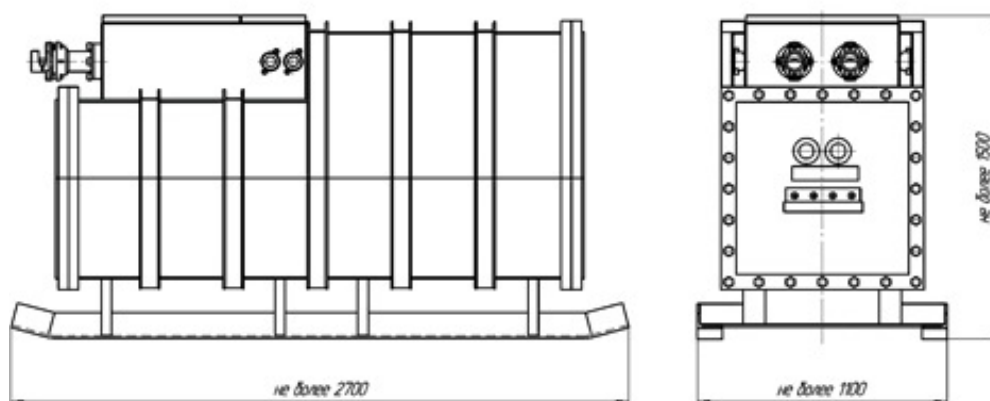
Габаритные размеры установки конденсаторной УКРВ-6,3-XXX-К-УХЛ5
